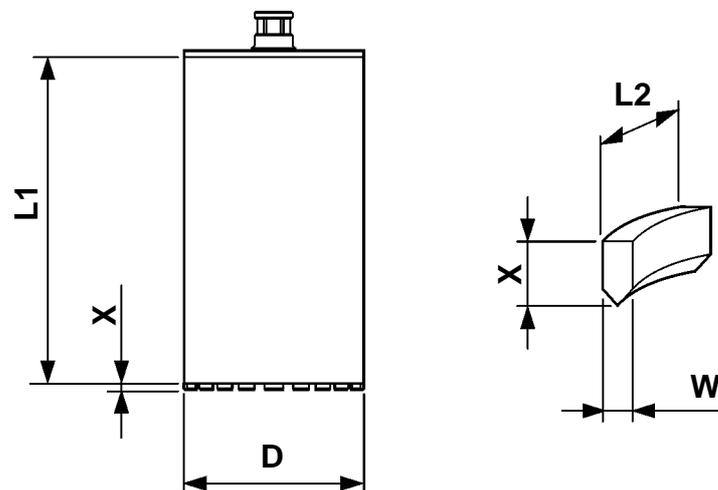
Dimensionierung einer Diamantbohrkrone
